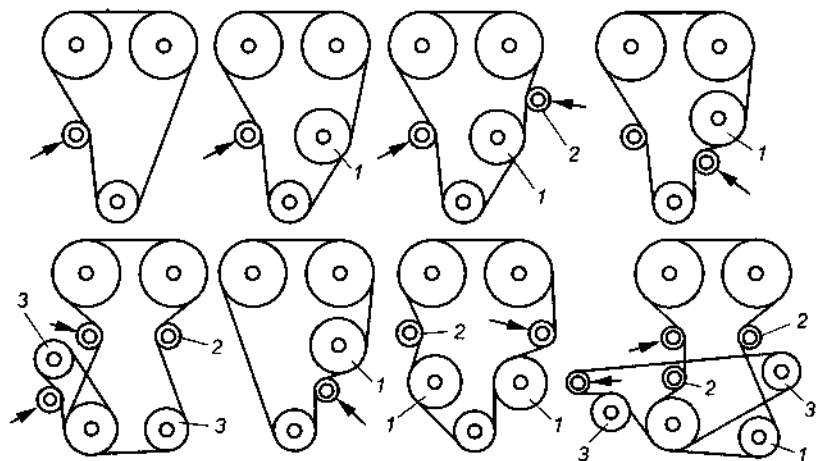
Различные конструкции приводов ГРМ с двумя верхними валами, в которых используются ремни: 1 — шкив привода вспомогательных агрегатов; 2 — паразитный ролик; 3 — шкив балансирующего вала
